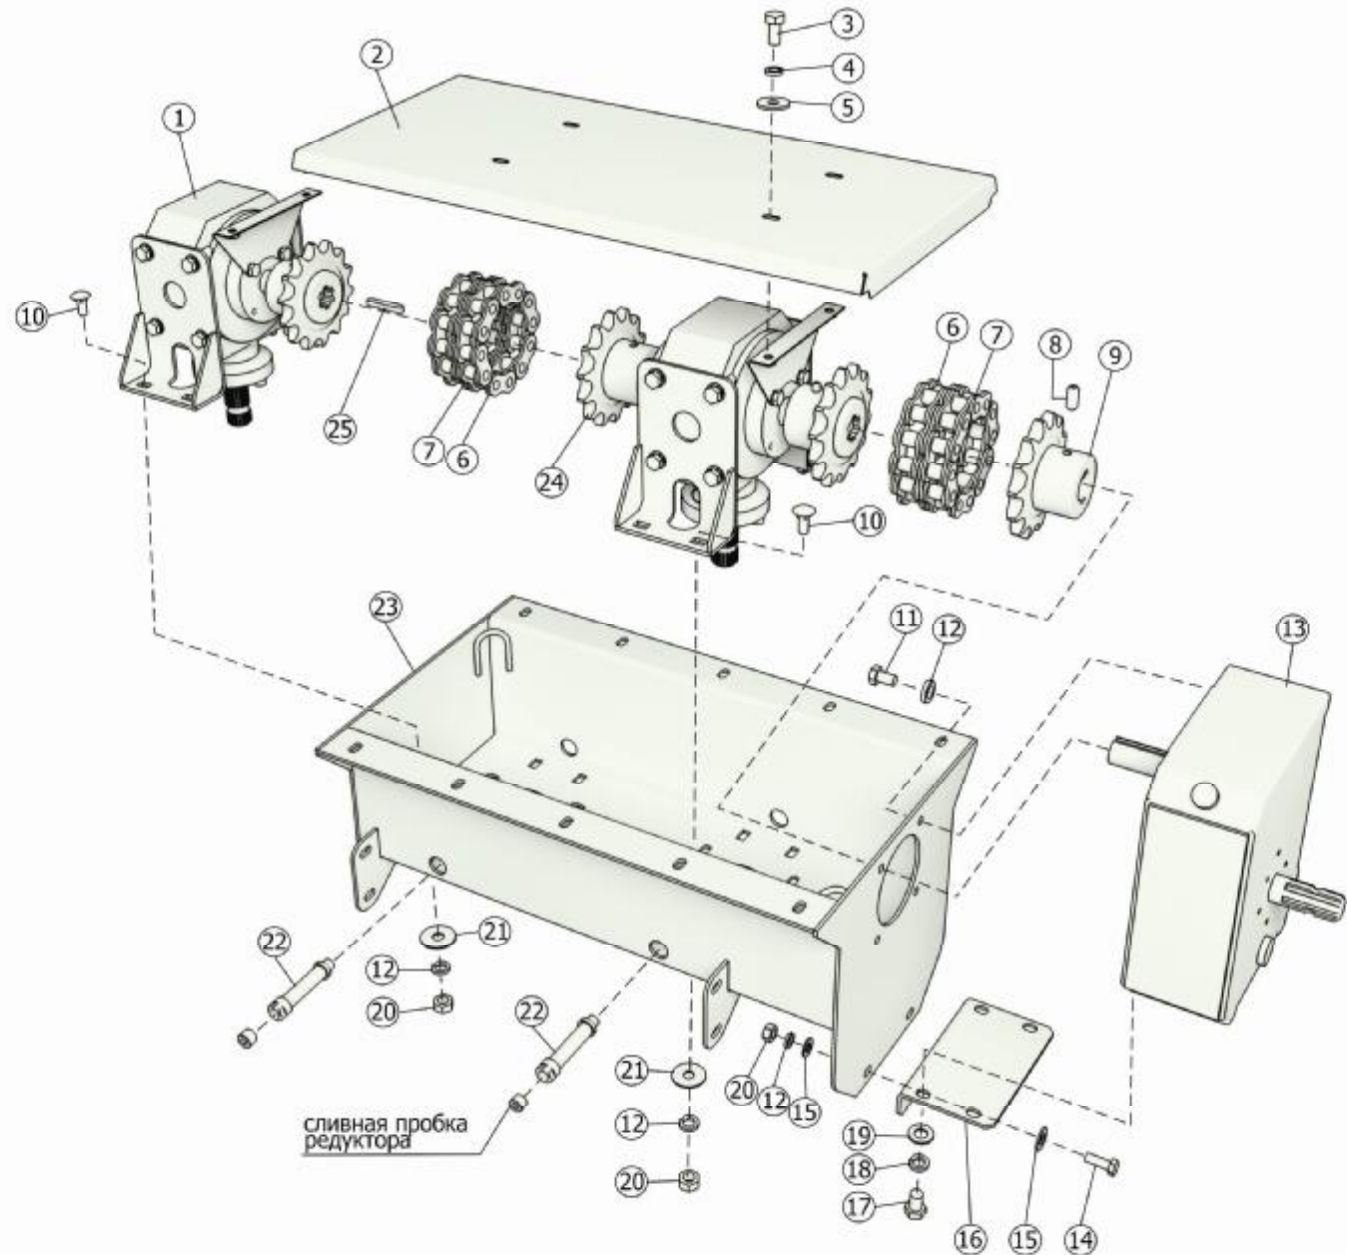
Блок редукторов ЖРН-601.03.00.000В
